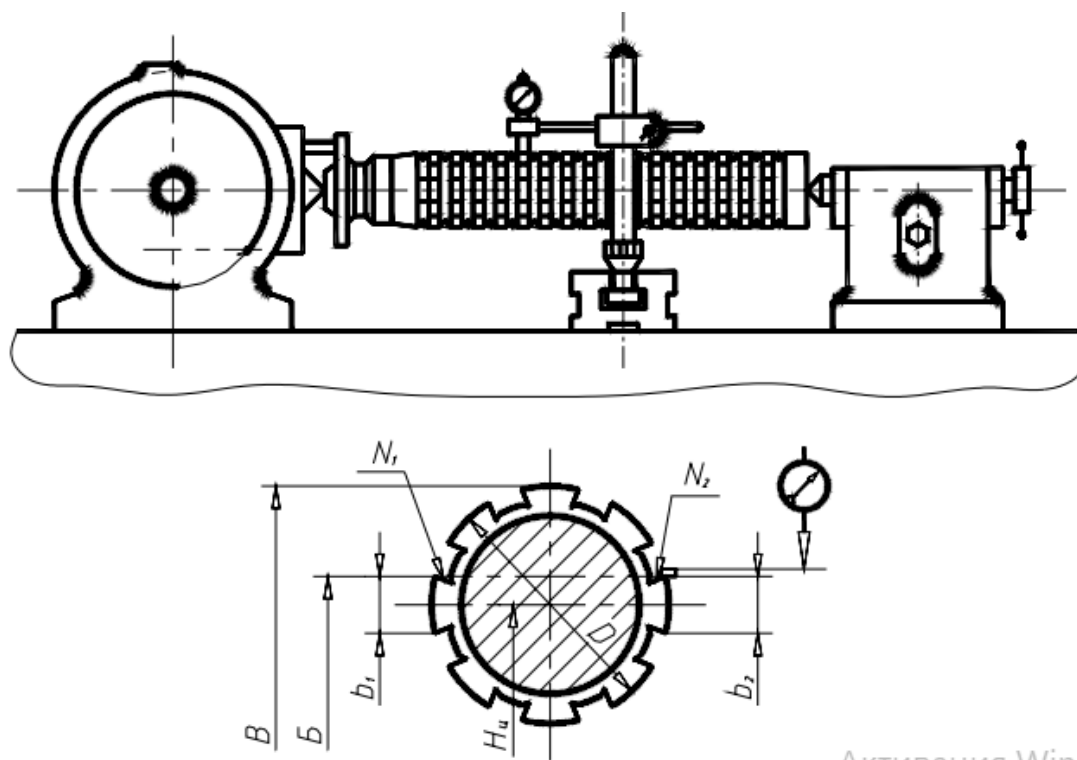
Схема контроля несимметричности расположения и погрешности шага шлицевых выступов зубьев протяжки
